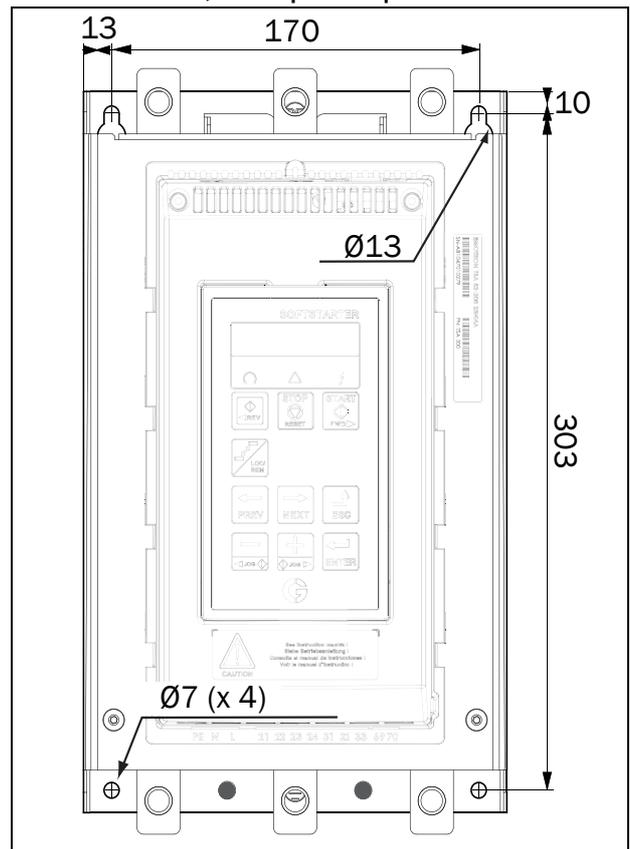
Расположение отверстий Emotron TSA, типоразмер 3.
